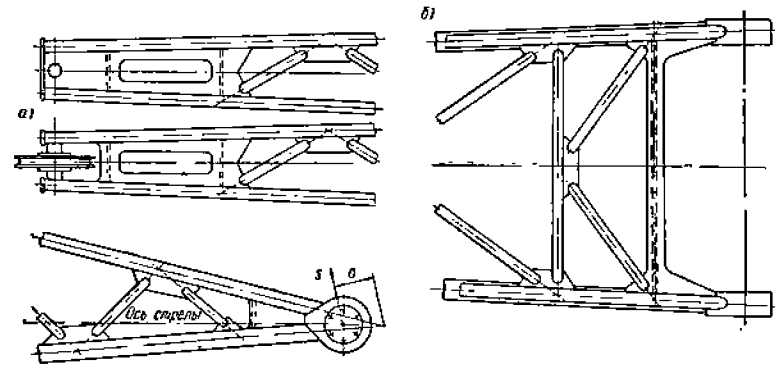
Оголовок (а) и опорный узел (б) стрелы трубчатой конструкции
